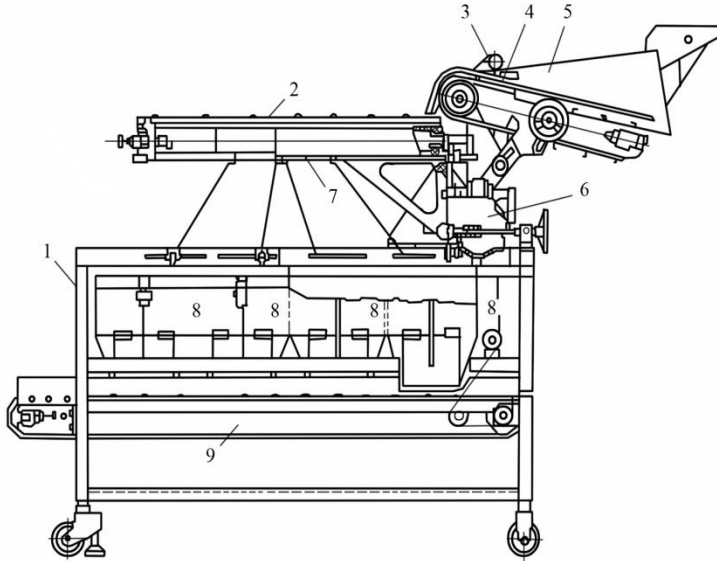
Універсальна калібрувальна машина: 1 – станина; 2 – калібрувальна головка; 3 – скидачі; 4 – вузькі стрічкові транспортери; 5 – завантажувальний бункер; 6 – привід; 7 – ступінчаті валки; 8 – збірники для відкаліброваного продукту; 9 – стрічковий транспортер
